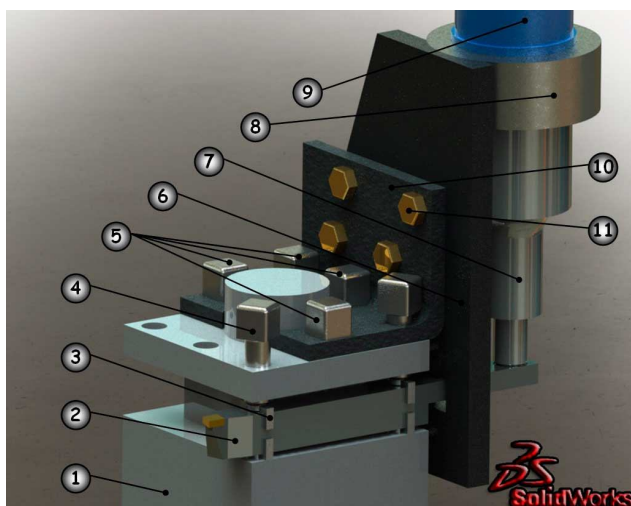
Экспериментальная установка для тангенциального направления колебаний: 1 – резцедержатель; 2 – резец; 3 – направляющие опоры; 4,5 – винты М14; 6 – стальной лист; 7 – концентратор ступенчатый; 8 – кольцо; 9 – преобразователь магнито-стрикционный; 10 – стальной уголок; 11 – винт М12
